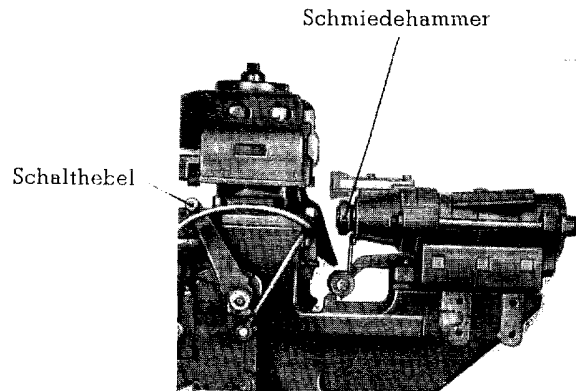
Maschine mit Schmiedehammer und Schalthebel, Lochhammer abgebaut
